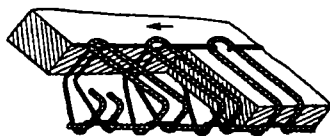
Строчка цепного обметочного стежка двухстрочная
